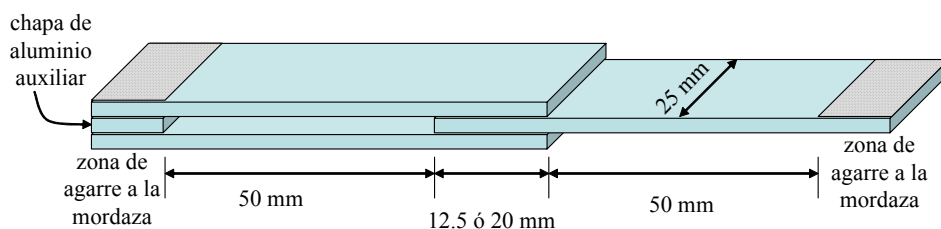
Esquema y dimensiones de las probetas fabricadas.
